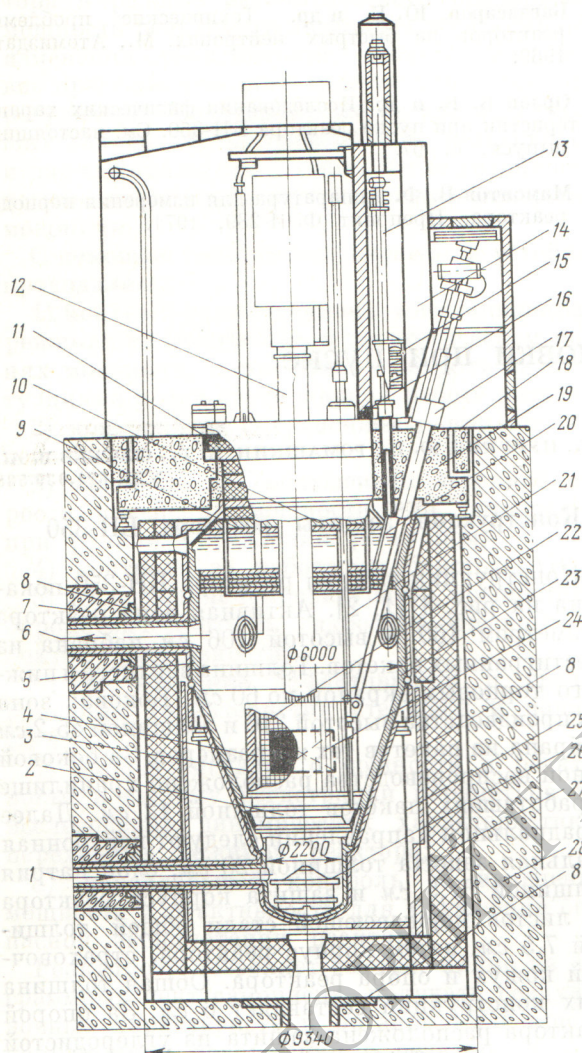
Продольный разрез реактора БН-350 с механизмами: 1 — вход натрия; 2 — напорный коллектор; 3 — стальные болванки; 4 — хранилище отработавших пакетов; 5 — корпус реактора; 6 — выход натрия; 7 — борированный бетон; 8 — стальная защита; 9 — большая поворотная пробка; 10 — малая поворотная пробка; 11 — защита из стали и графита; 12 — центральная колонна с перегрузочными СУЗ; 13 — механизм передачи пакетов; 14 — перегрузочный бокс; 15 — чугунная дробь; 16 — уран; 17 — элеватор; 18 — защитная пробка; 19 — верхняя неподвижная защита (бетон); 20 — уровень натрия; 21 — механизм перегрузки; 22 — зона восприимчивости; 23 — тепловая защита; 24 — активная зона; 25 — опора реактора; 26 — страховочный кожух; 27 — боковая защита (железорудный концентрат); 28 — бетонная защита.
